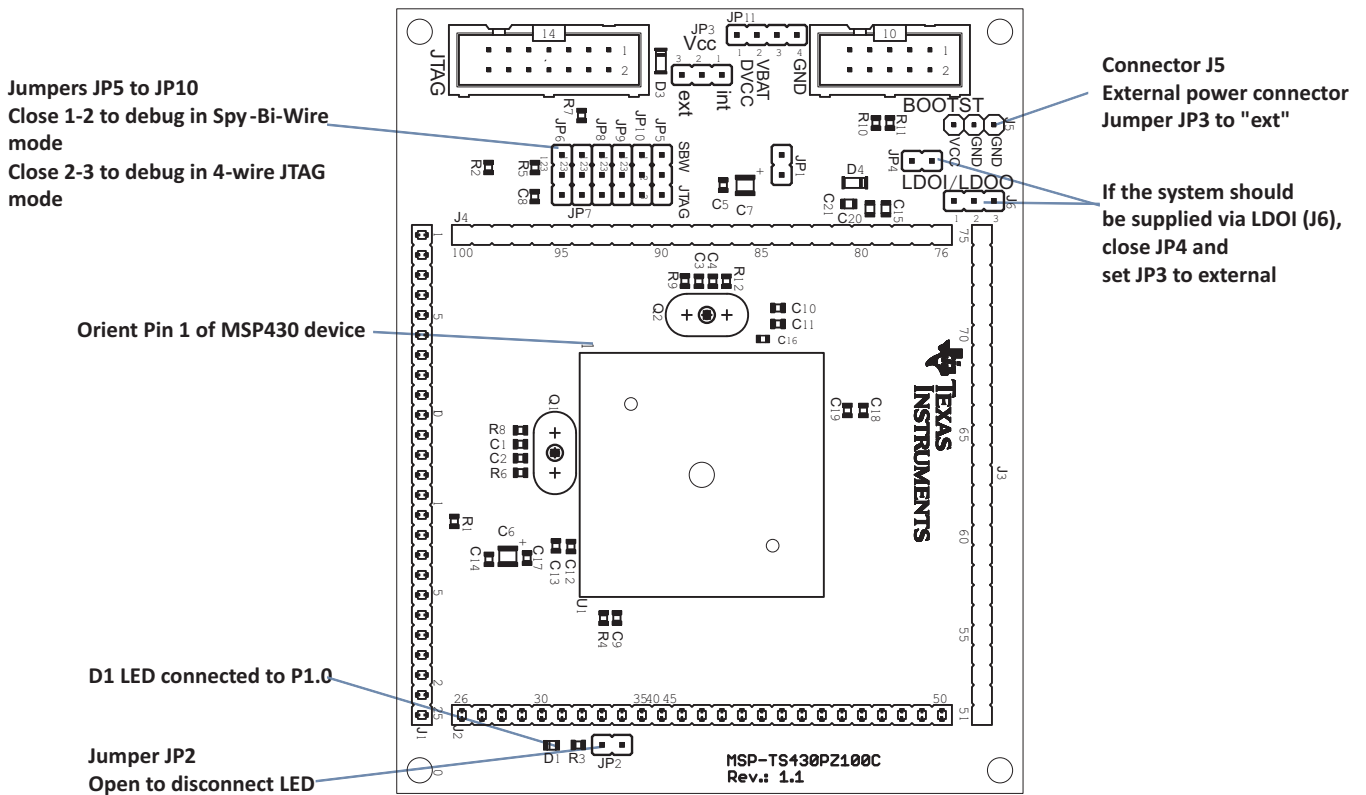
MSP-TS430PZ100C 目标插座模块, PCB
